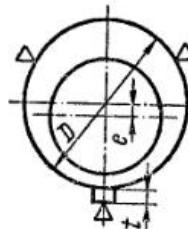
Обтачивание эксцентриковых заготовок в самоцентрирующем патроне
